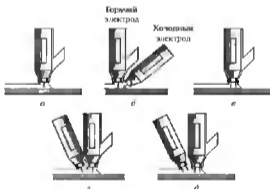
Различные методы сварки под флюсом:
